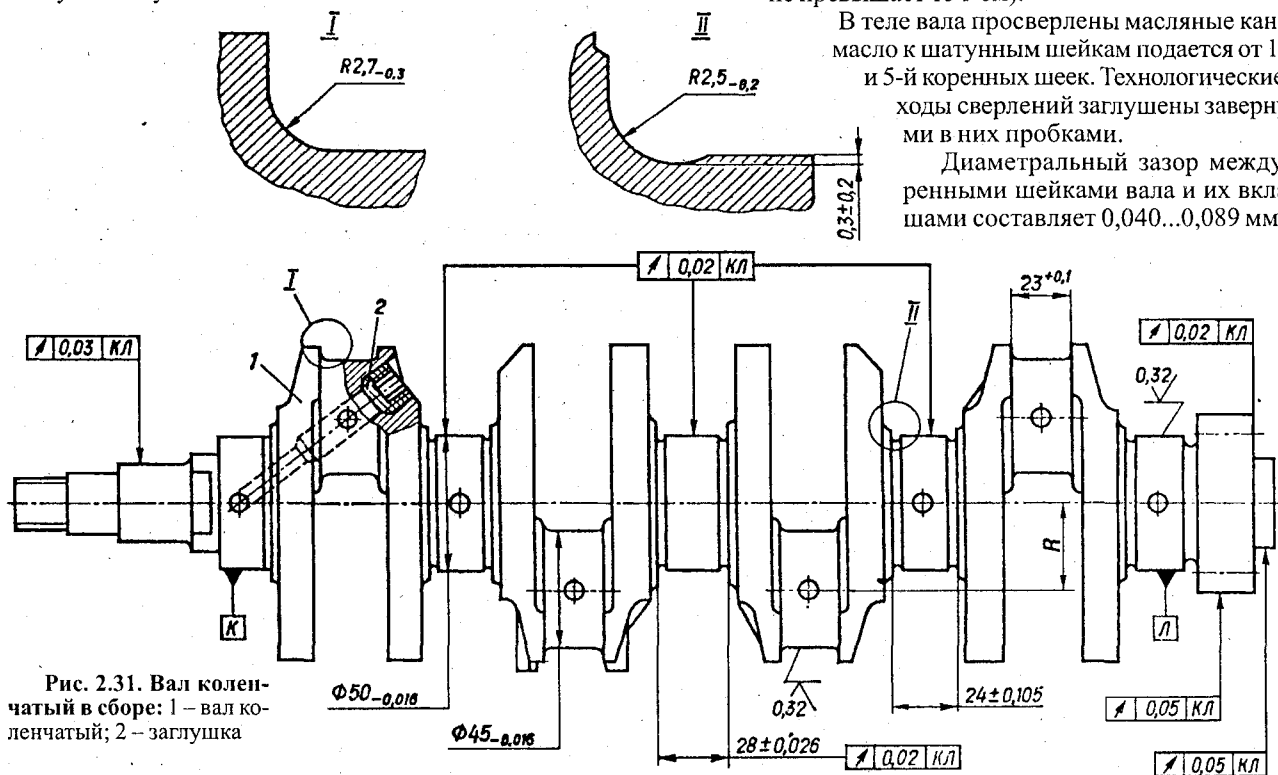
Вал коленчатый в сборе: 1 – вал коленчатый; 2 – заглушка
